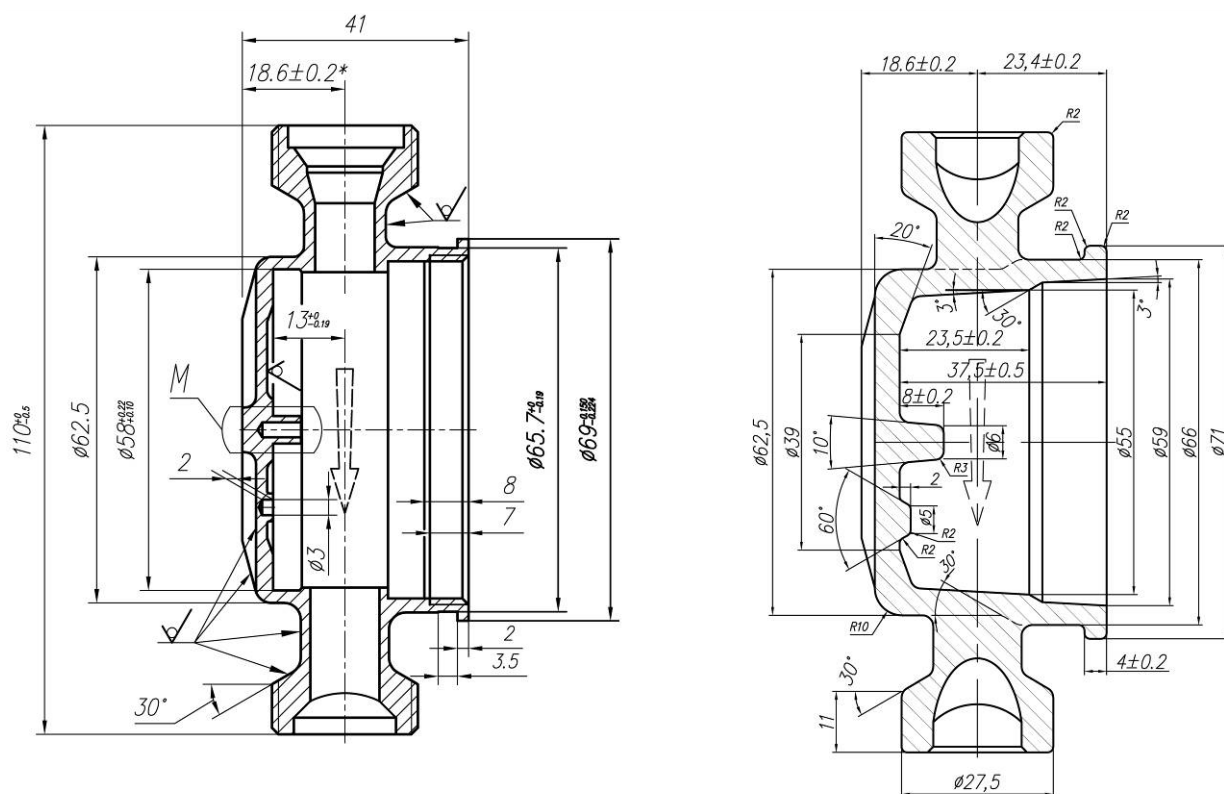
Ескіз виливка корпусу лічильника води
